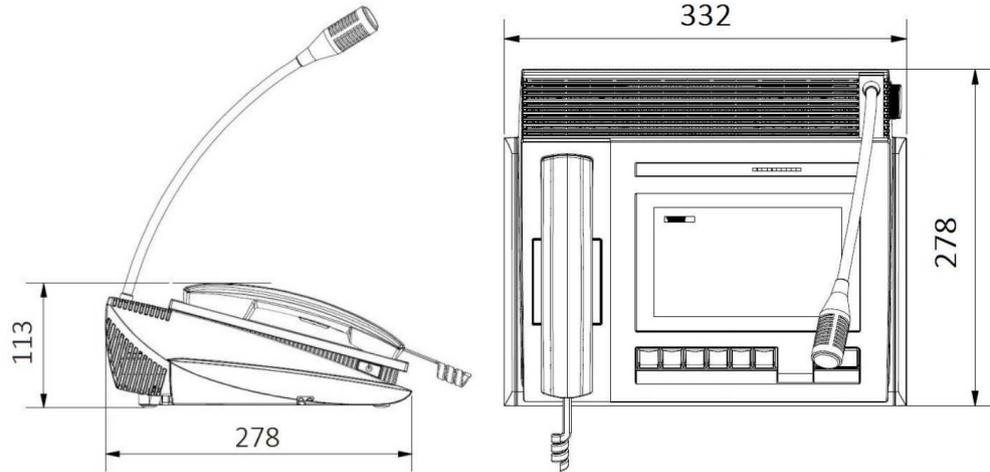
IP-3102/IP-3108 - Dimensions physiques en mm
